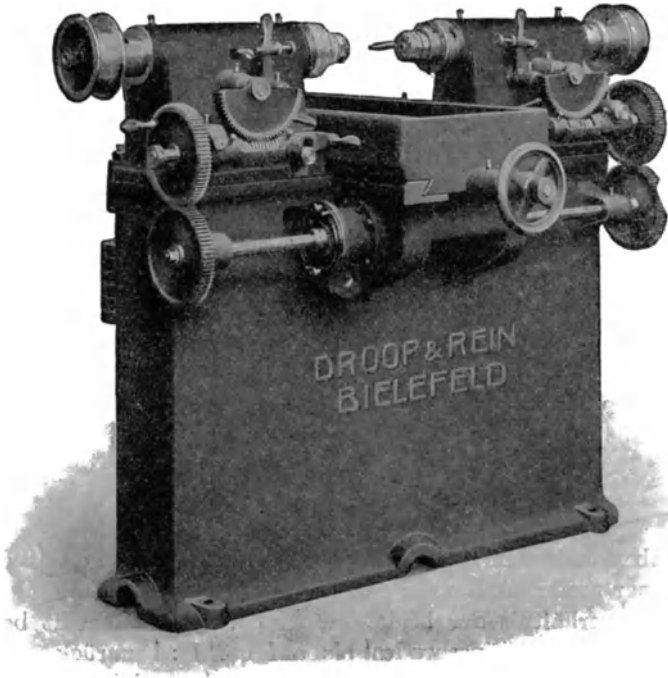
Die Keillochfräsmaschine von Droop & Rein.
